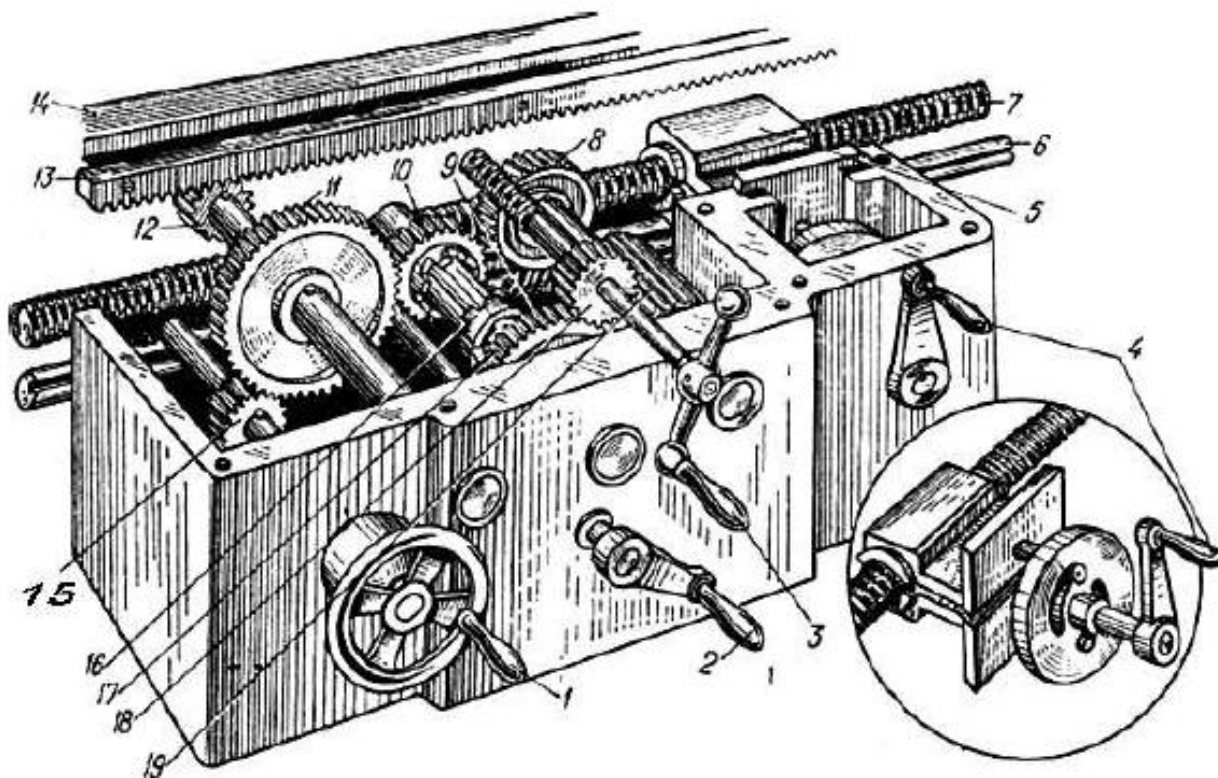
Фартух 1, 2, 3, 4 – рукоятка, 5 – маточна гайка; 6 – ходовий валик; 7 – ходовий гвинт; 8 – черв'ячне колесо; 9 – черв'як; 10, 11, 15, 17, 18, 19 – зубчасті колеса; 12 – рейкове зубчасте колесо; 13 – рейка; 14 – станина; 16 – муфта.
